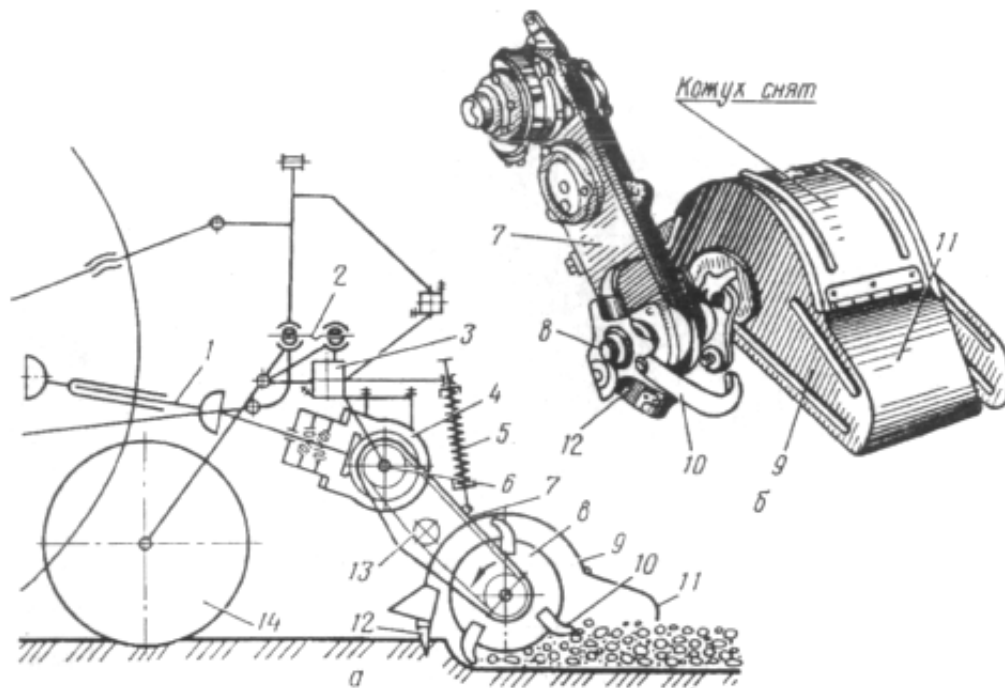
Фрезерный культиватор КФ-5,4:
